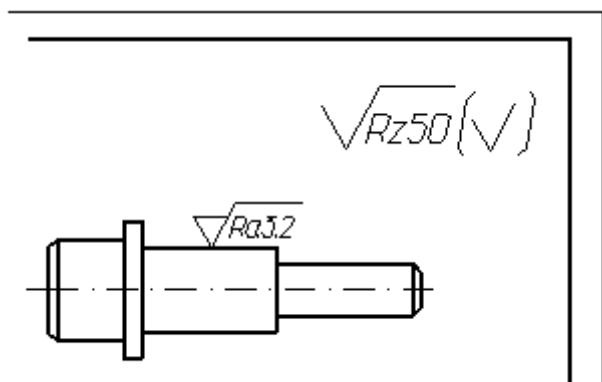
Указание шероховатости одинаковой для части поверхностей изделия
